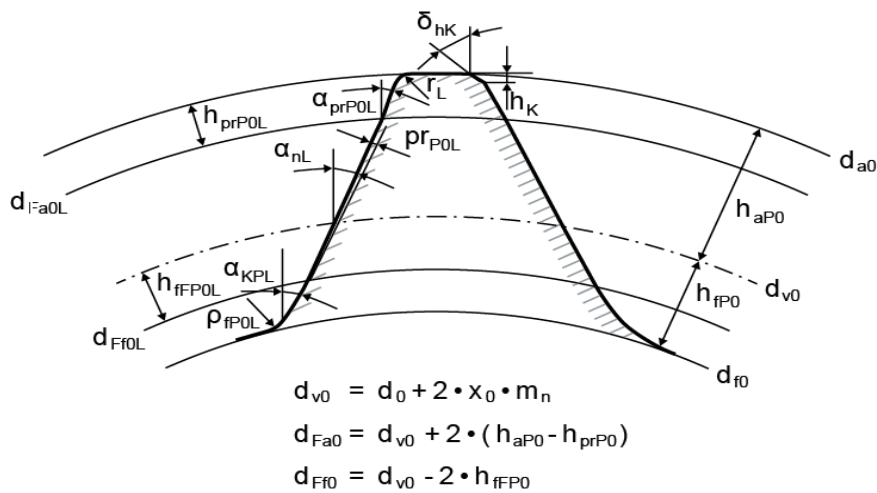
Bezugsprofil für asymmetrische Zahnräder für die Konfiguration Werkzeug: Stossrad
